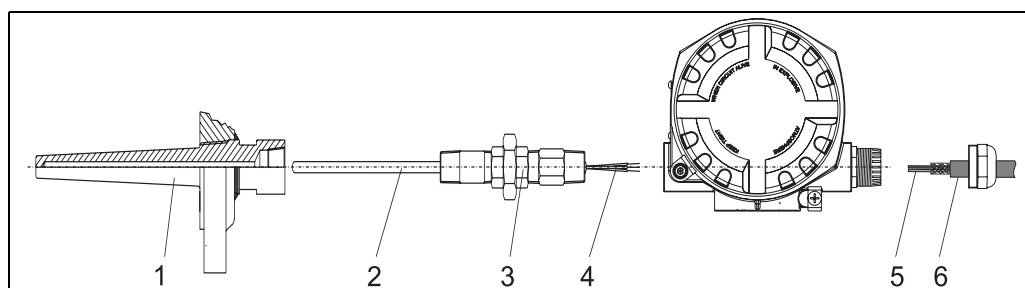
Installazione del trasmettitore da campo direttamente su un sensore
